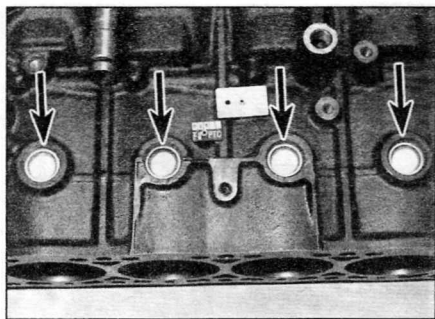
Стержневые заглушки блока цилиндров (отмечены стрелками)
